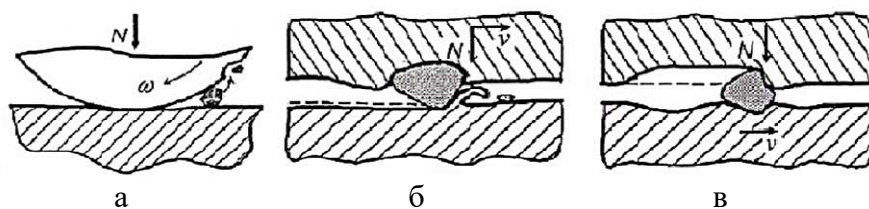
Механізми зношування деталей вільними абразивними частками
